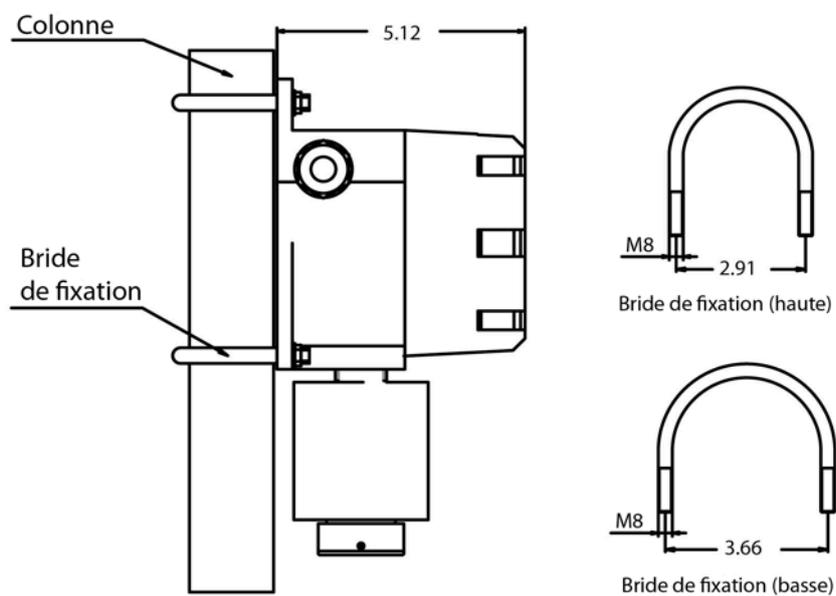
Installation de l' iTRANS-2 sur un poteau à l'aide de boulons en « U ».
